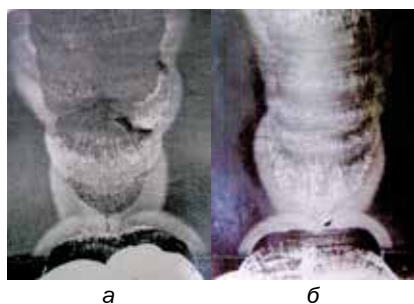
Поднаплавочная трещина и непровар в корне перлитной части сварного шва плакированного трубопровода Ду 800 мм (макрошлифы)
